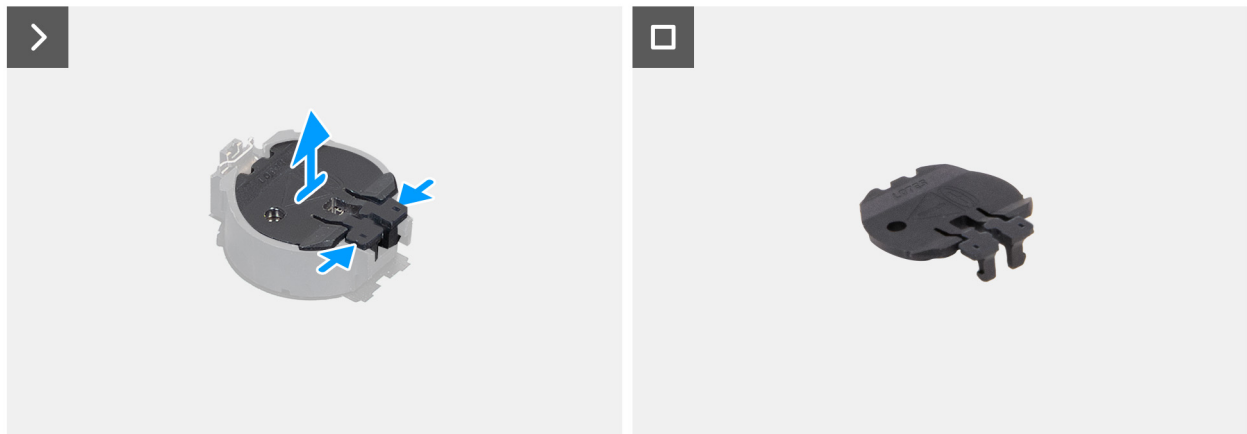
Extracción de la cubierta de la batería de tipo botón
